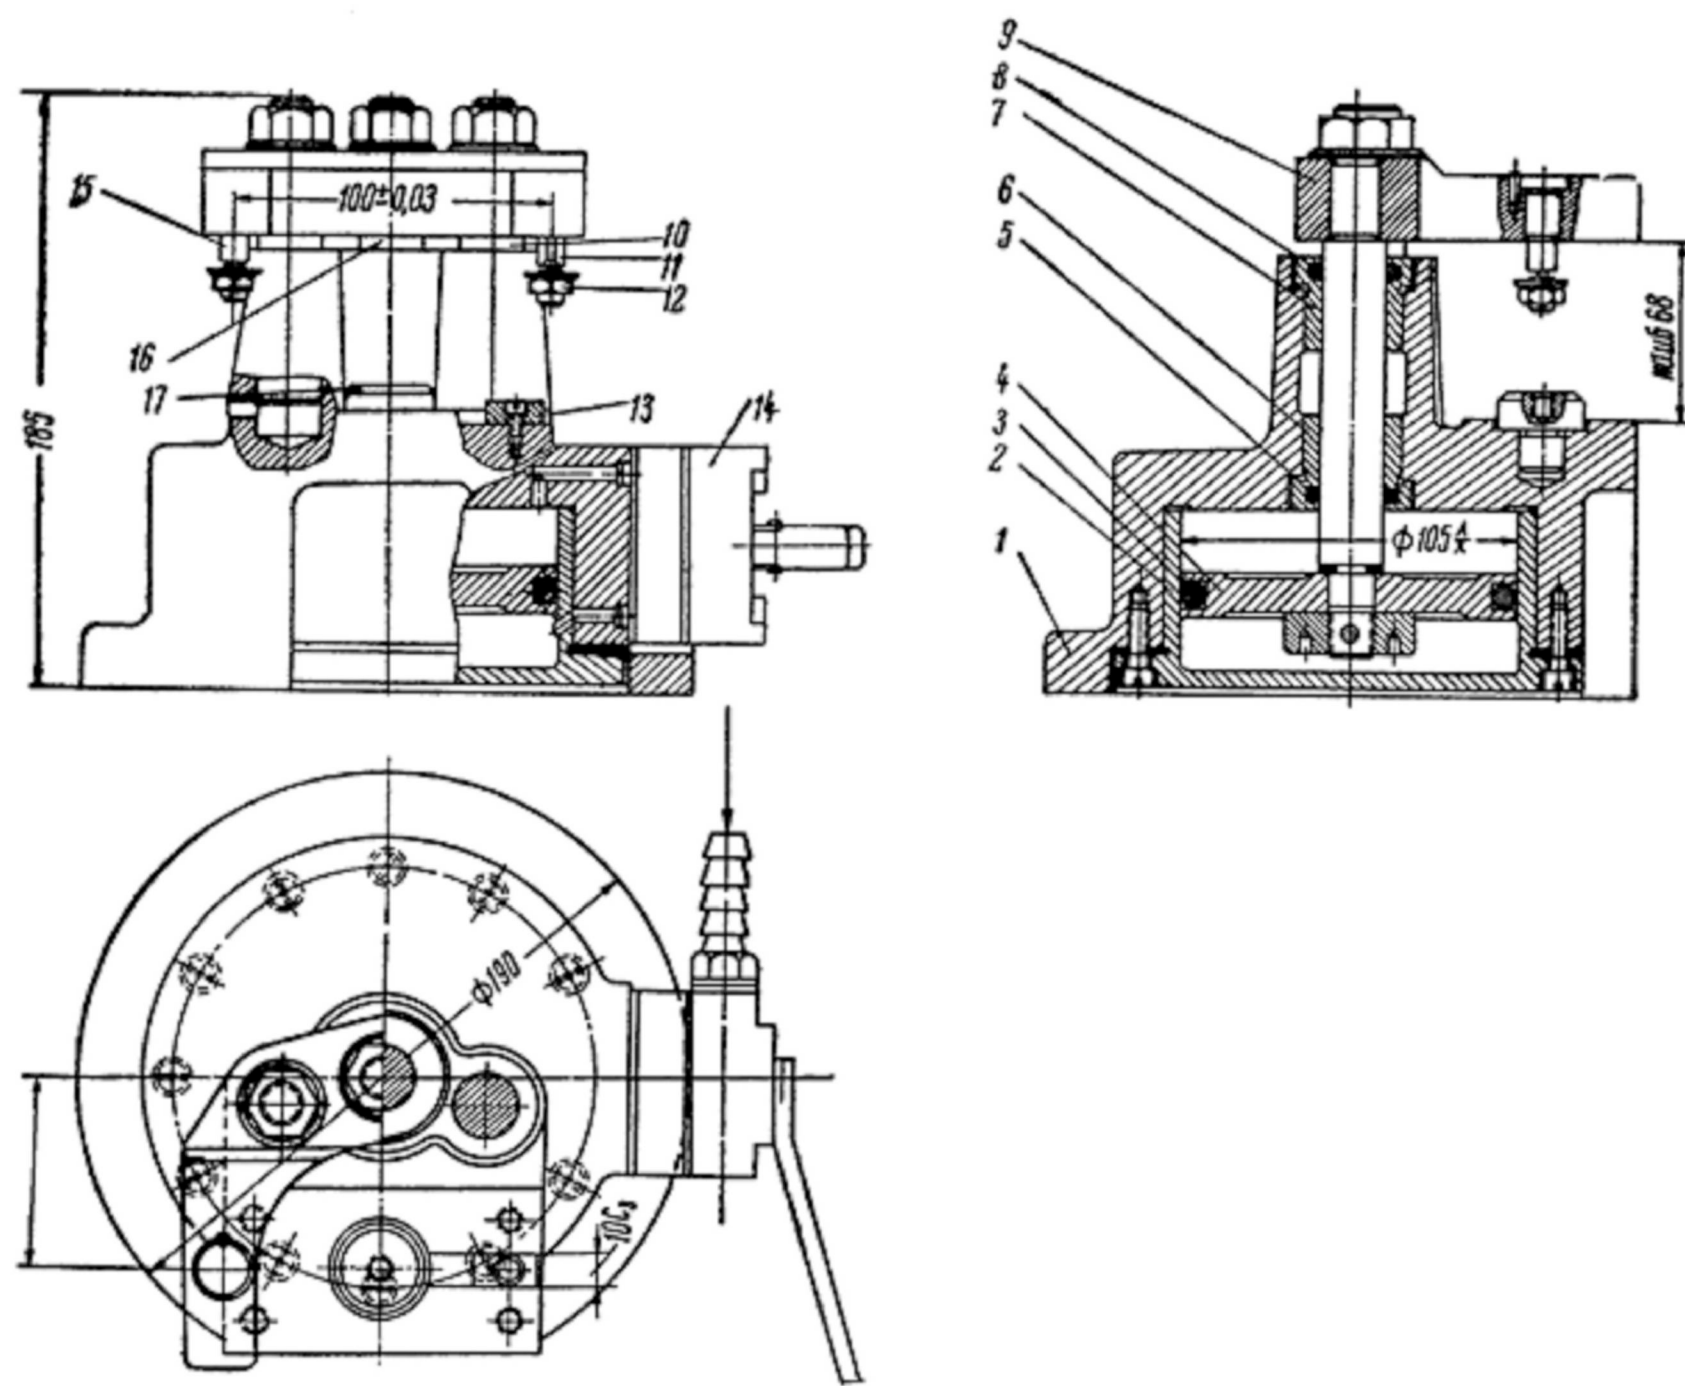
Скальчастий кондуктор консольного типу з пневматичним приводом
